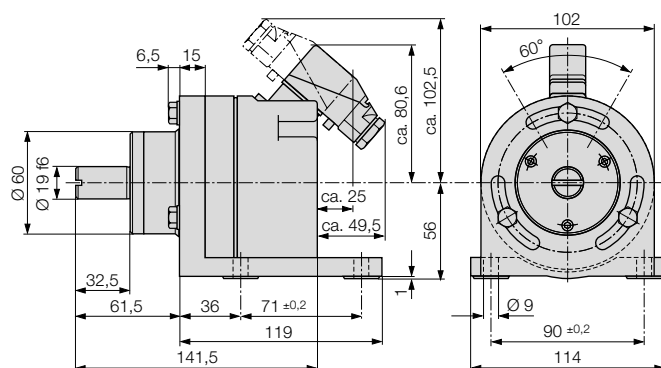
KINAX WT 707 mit Steckverbinder und Fuss.
